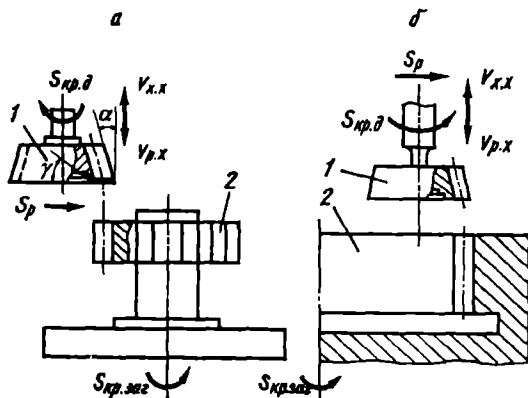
Схемы нарезания зубчатых колес зубодолблением:
